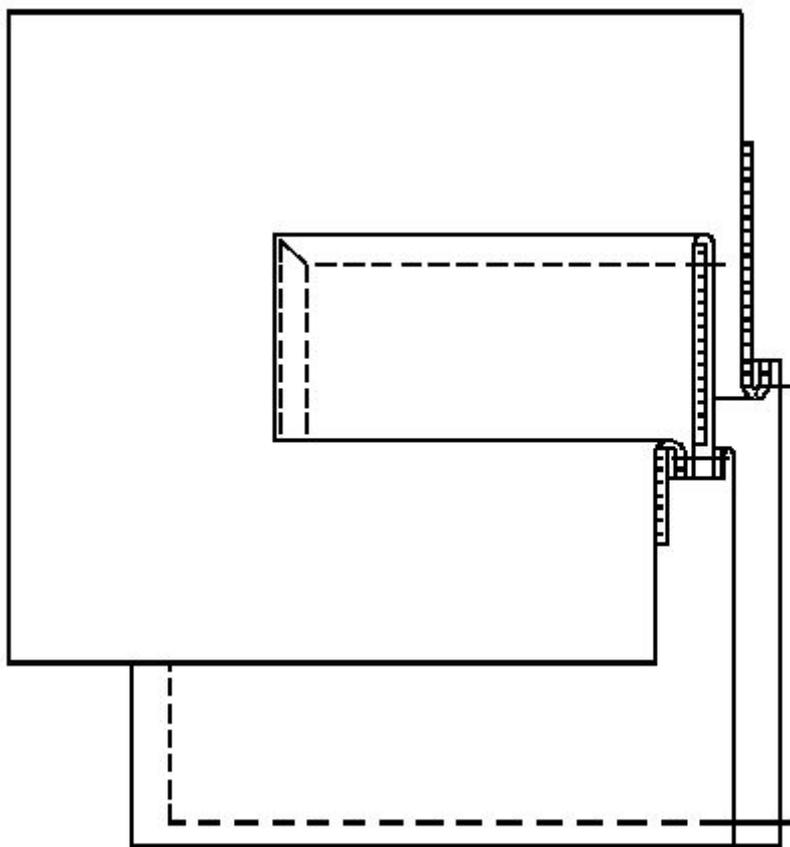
Схема метода поузловой обработки бокового прорезного кармана с листочкой с настрочными концами
